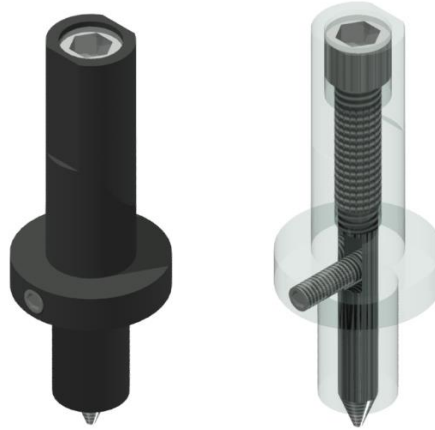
Vista tridimensional do desenho 3D CAD do Pino da Ferramenta.
